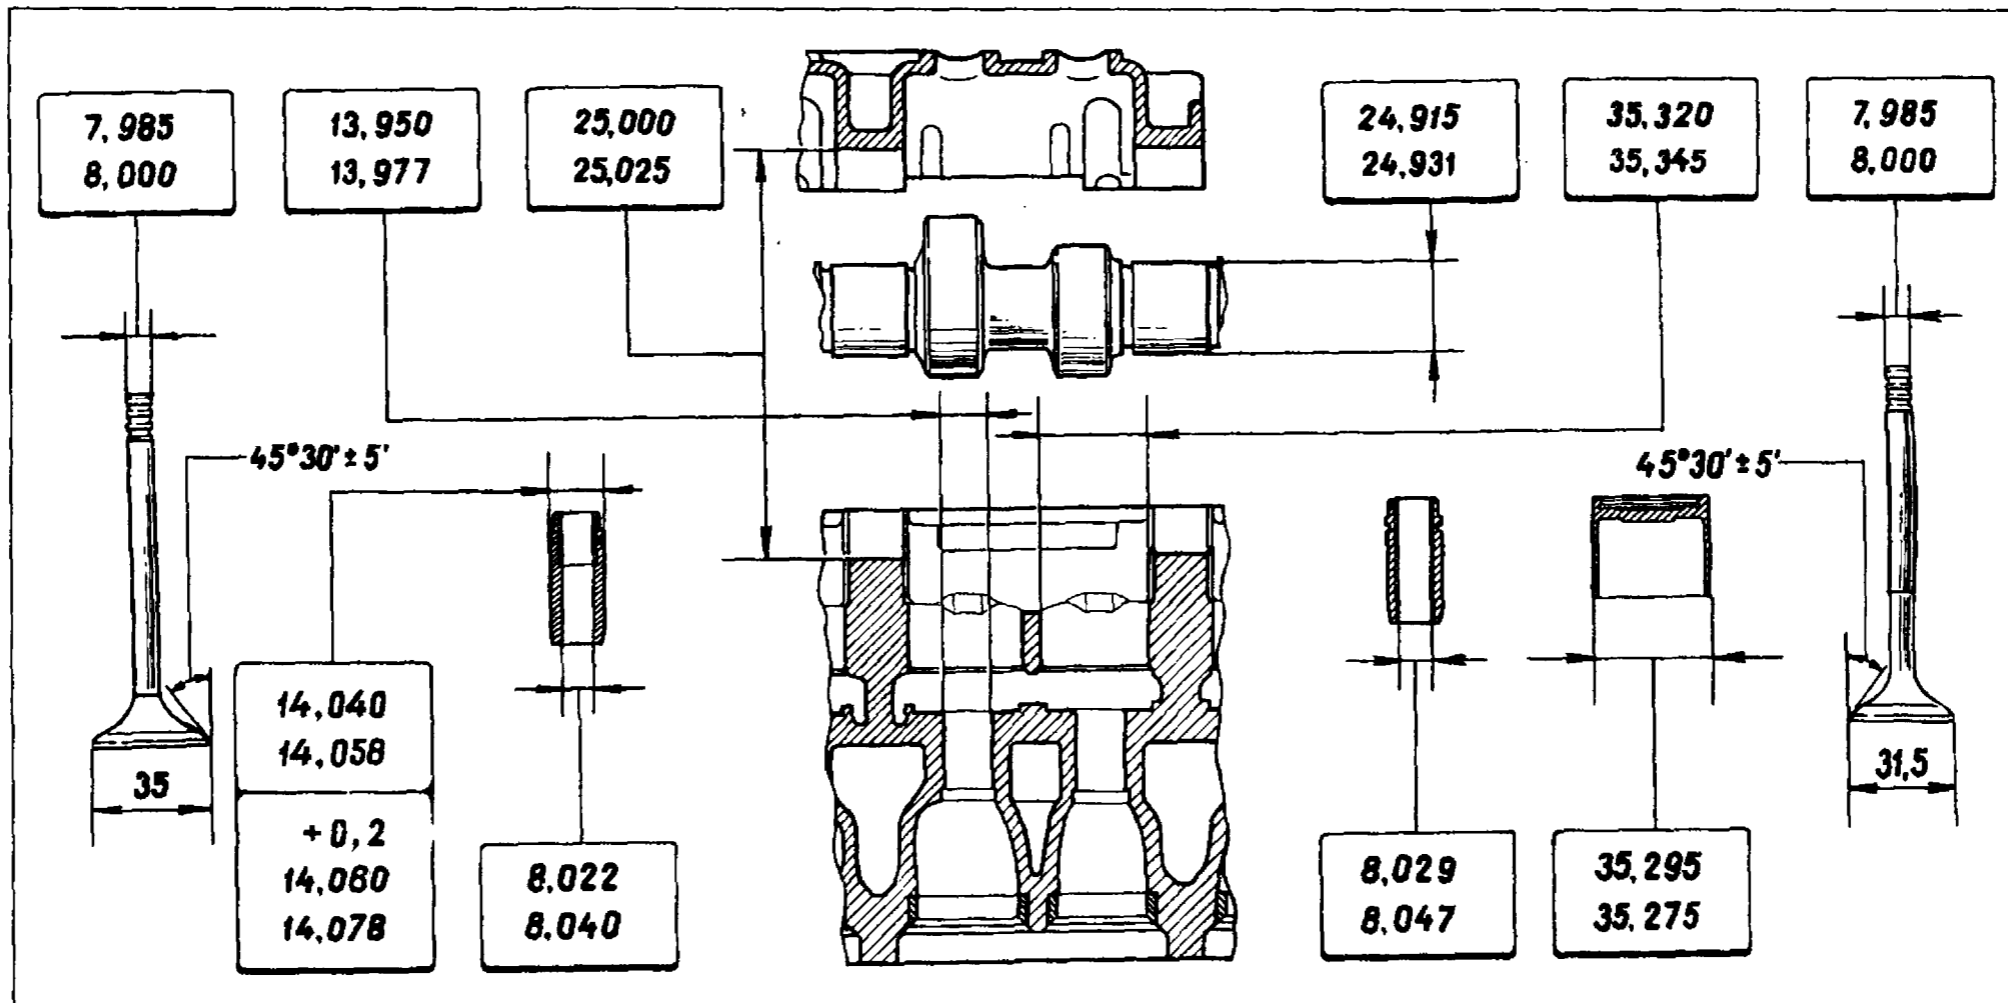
Основные размеры головки блока цилиндров и деталей механизма привода клапанов
